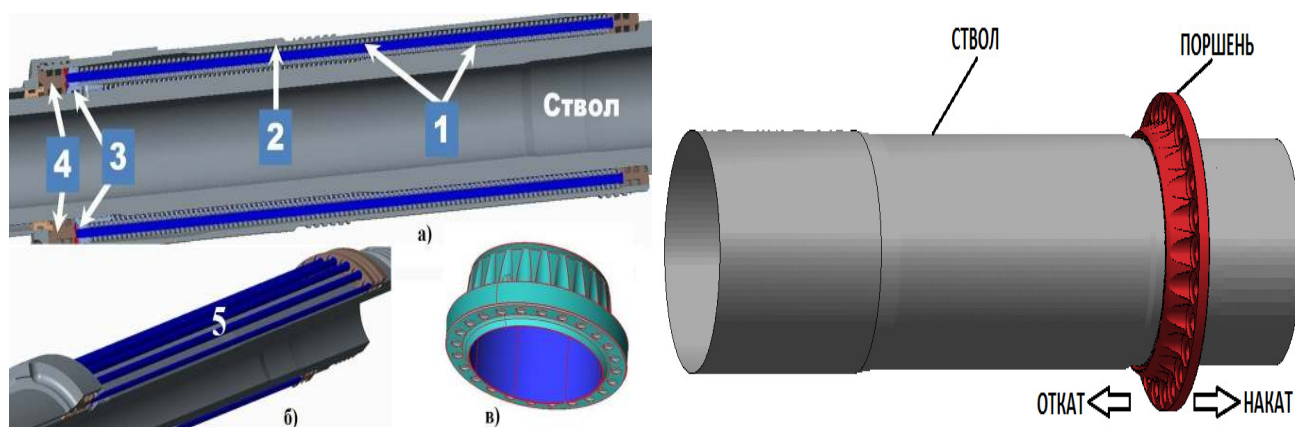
Слева: Общая схема гидротормоза пушечной установки: а) — Общая схема (1 - цилиндр с рабочей жидкостью с направляющими и пружинами; 2 — кожух, 3 — поршень, 4 - сальники); б) — общая схема без кожуха (5 — направляющие); в) — поршень; справа — принципиальная схема работы
